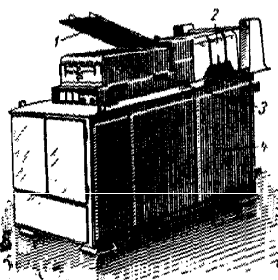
Нагреватель фирмы «Асек» для нагрева заготовок в атмосфере нейтрального газа:
